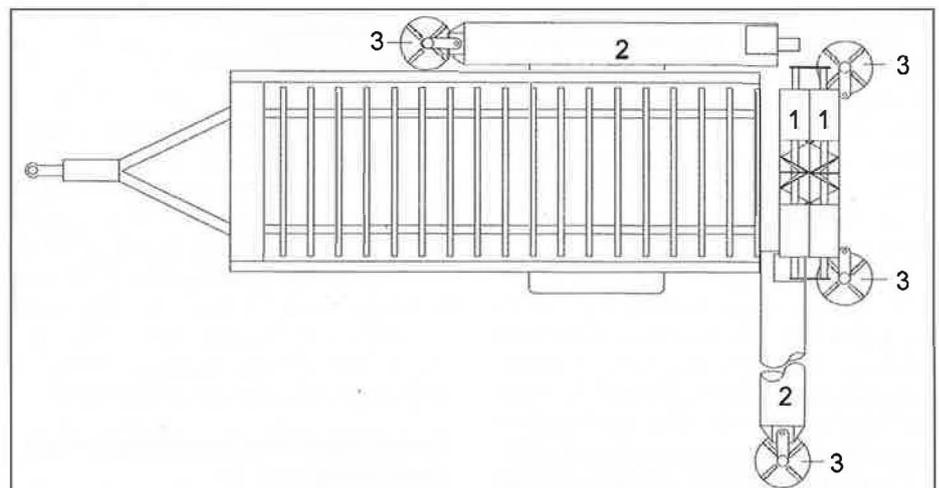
Prinzipskizze der Draufsicht: 1-Dosierschnecken, 2-Transportschnecken, 3-Drehteller
